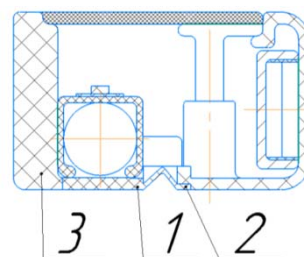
Соединение крышки для батареек и каркаса: 1 – крышка для батареек; 2 – разъемное замковое соединение; 3 – каркас
